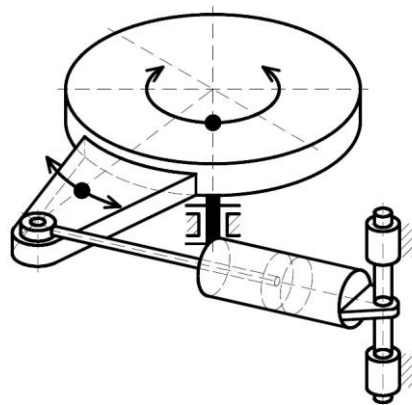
Rotační motor – kývný pohyb2 [2]
